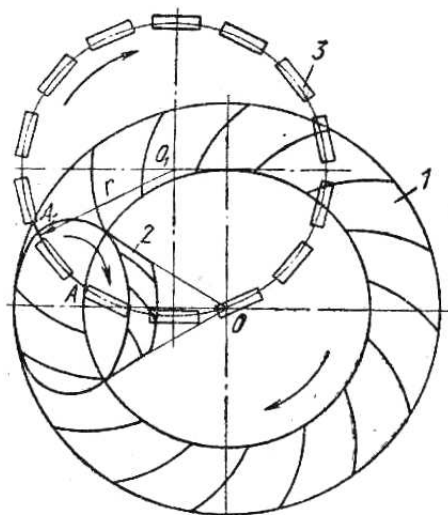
Схема нарезания конических колес с круговыми зубьями
